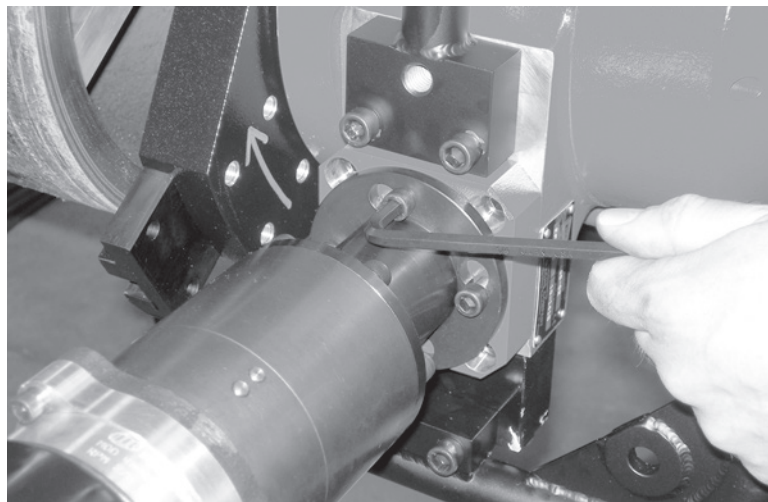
Ruotare la flangia per inserire le viti nelle rispettive sedi, quindi serrare le viti.
